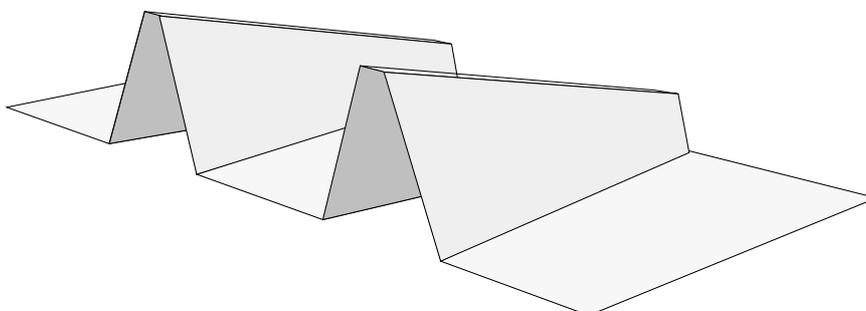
Abänderung der oben beschriebenen SOLight-Variante, welche mit einer aufgebogenen Platte fundiert wird. Anstelle der Halteklammern wird das Formteil direkt aufgebogen.
